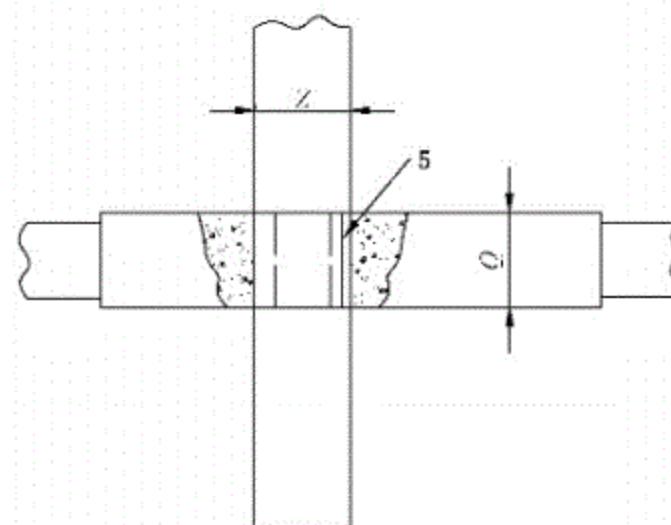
焊接接头准静态断裂韧度试样焊板取样方位
